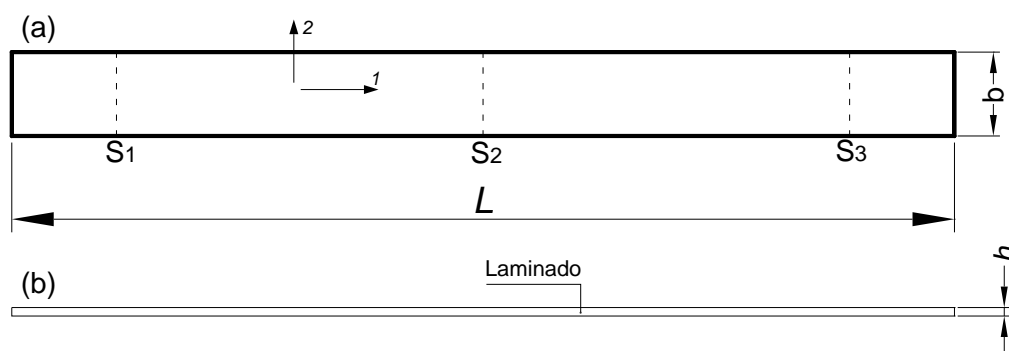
Geometria, eixos, secções e dimensões dos provetes MDL para os ensaios de arranque: (a) vista em planta; (b) corte.
